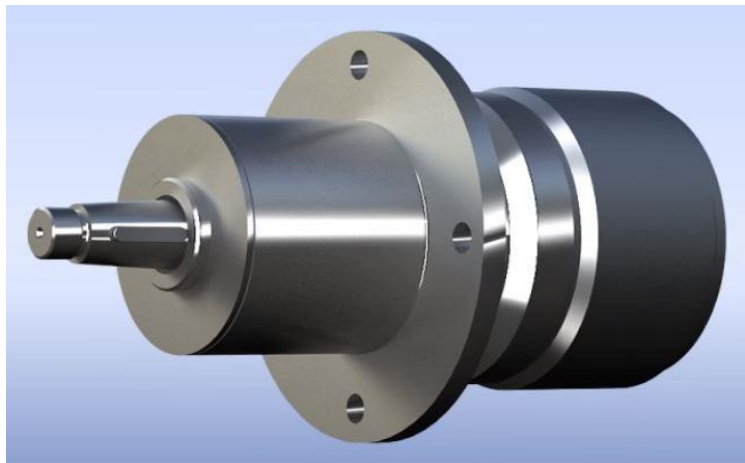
Волновой редуктор с промежуточными телами качения.
